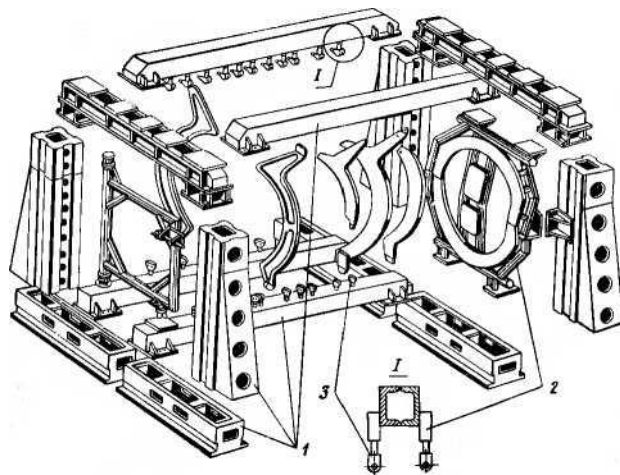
Основные элементы конструкции приспособления для сборки отсека фюзеляжа:
